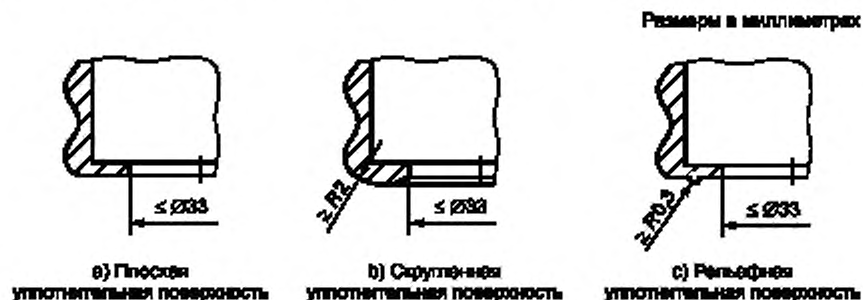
Уплотнительная поверхность соединителя с наружной резьбой
